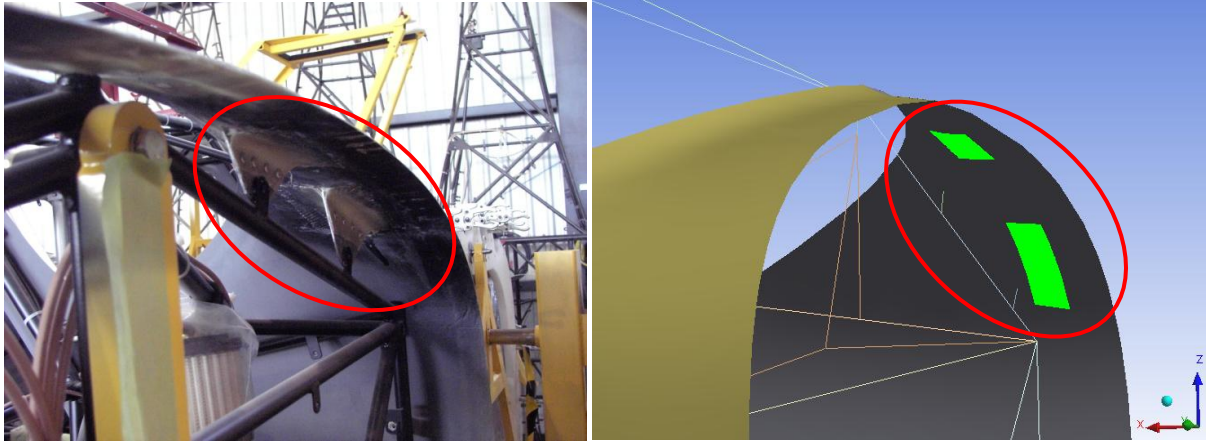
Modélisation par un joint d'un assemblage fait avec une plaque de support
